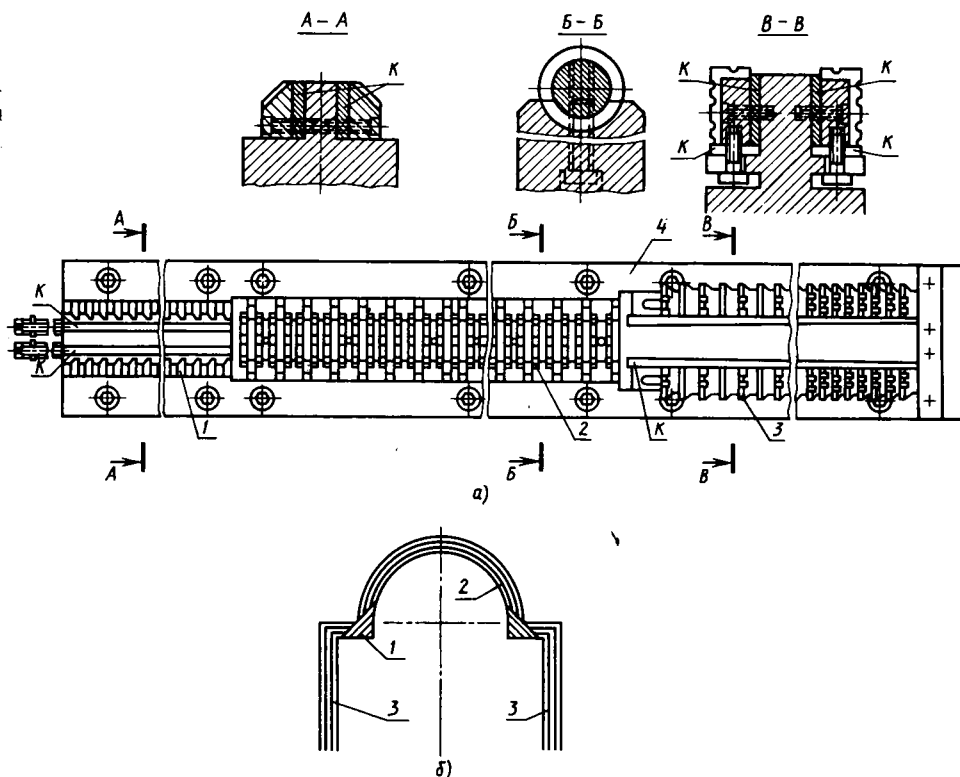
Протяжка для обработки наружных поверхностей (а) и схема резания (б)
